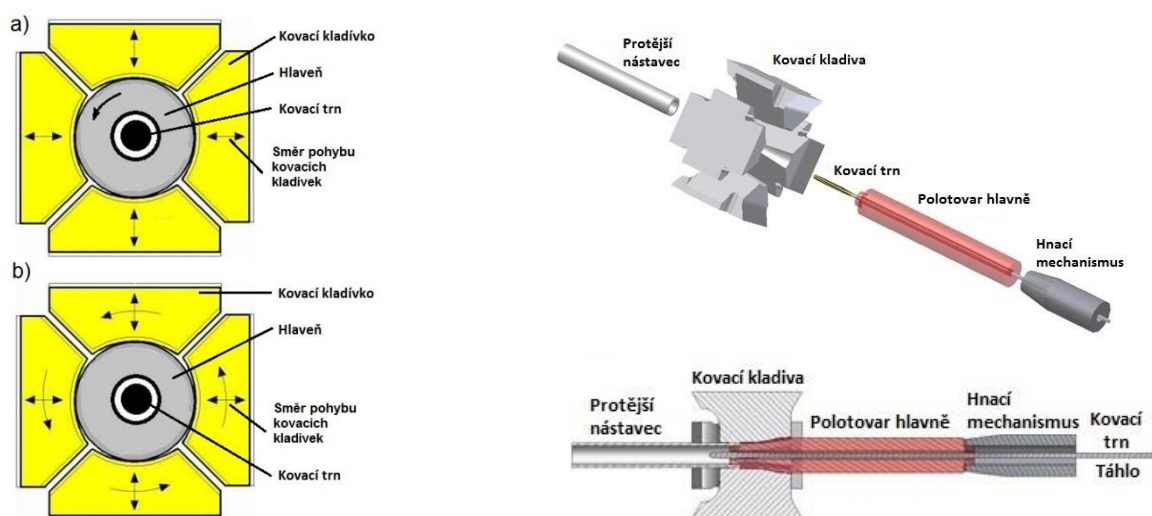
Kovací kladívko (kovátko)²¹.
